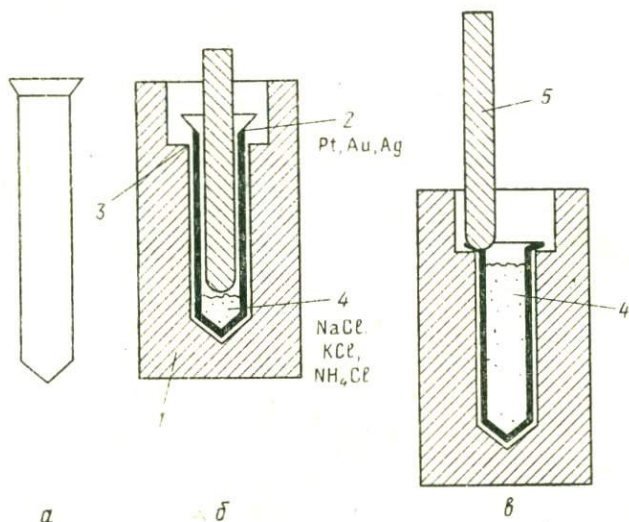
Футеровка рабочего объема автоклава вкладышем из благородных металлов: а — вкладыш, б — опрессовка вкладыша заполнением его солью (начальная стадия), в — отбортовка вкладыша; 1 — корпус автоклава, 2 — вкладыш, 3 — уступ автоклава, на который загибается борт вкладыша, 4 — соль, 5 — оправка
